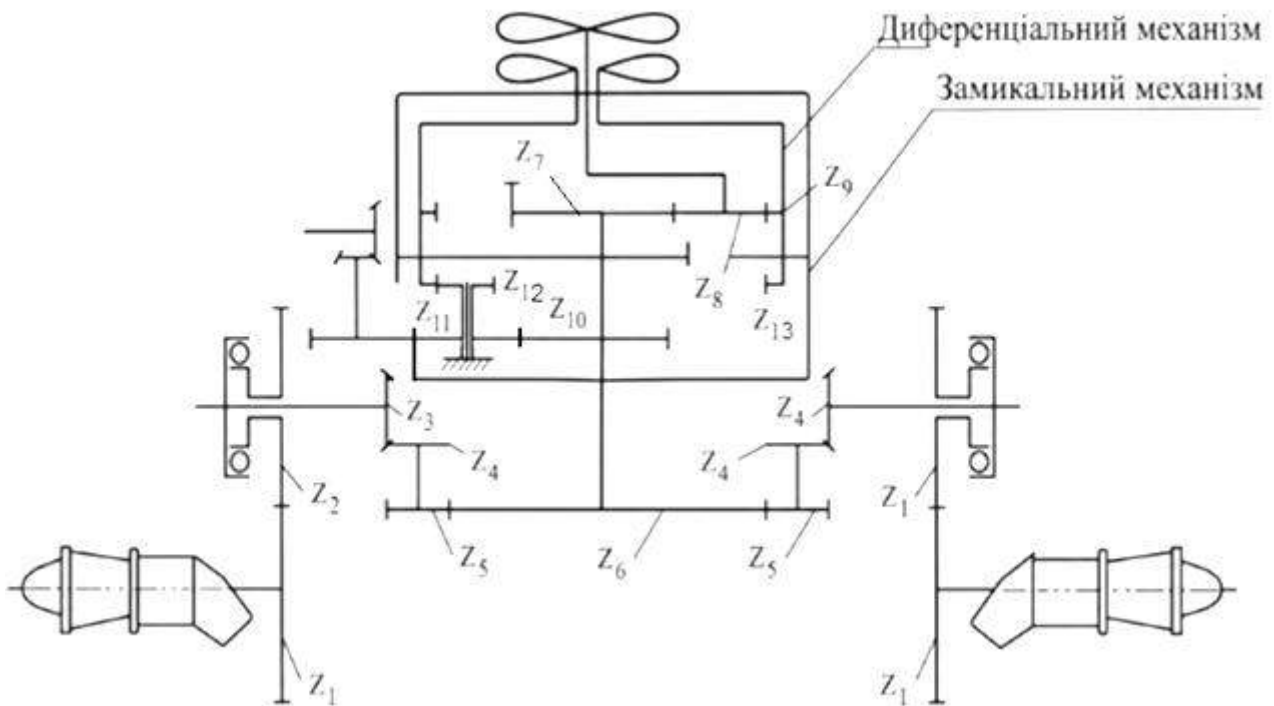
Кінематична схема вертолітного редуктора РВ-3Ф
